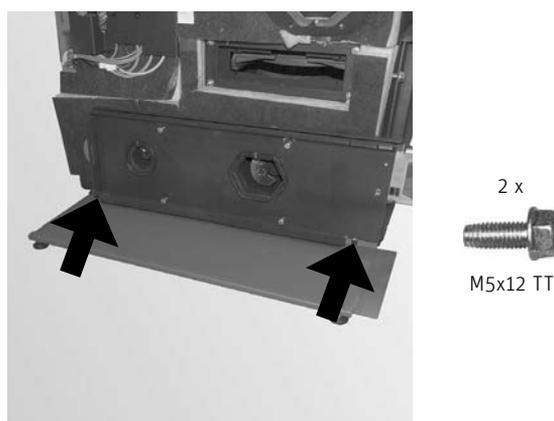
Fissare il pannello a pavimento con 2 viti M5x12 TT
